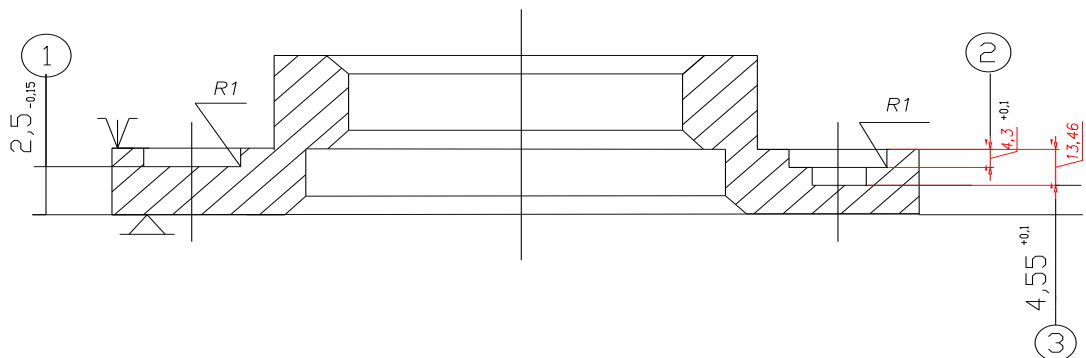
Ескіз обробки деталі «Кільце» на фрезерну операцію з ЧПУ
